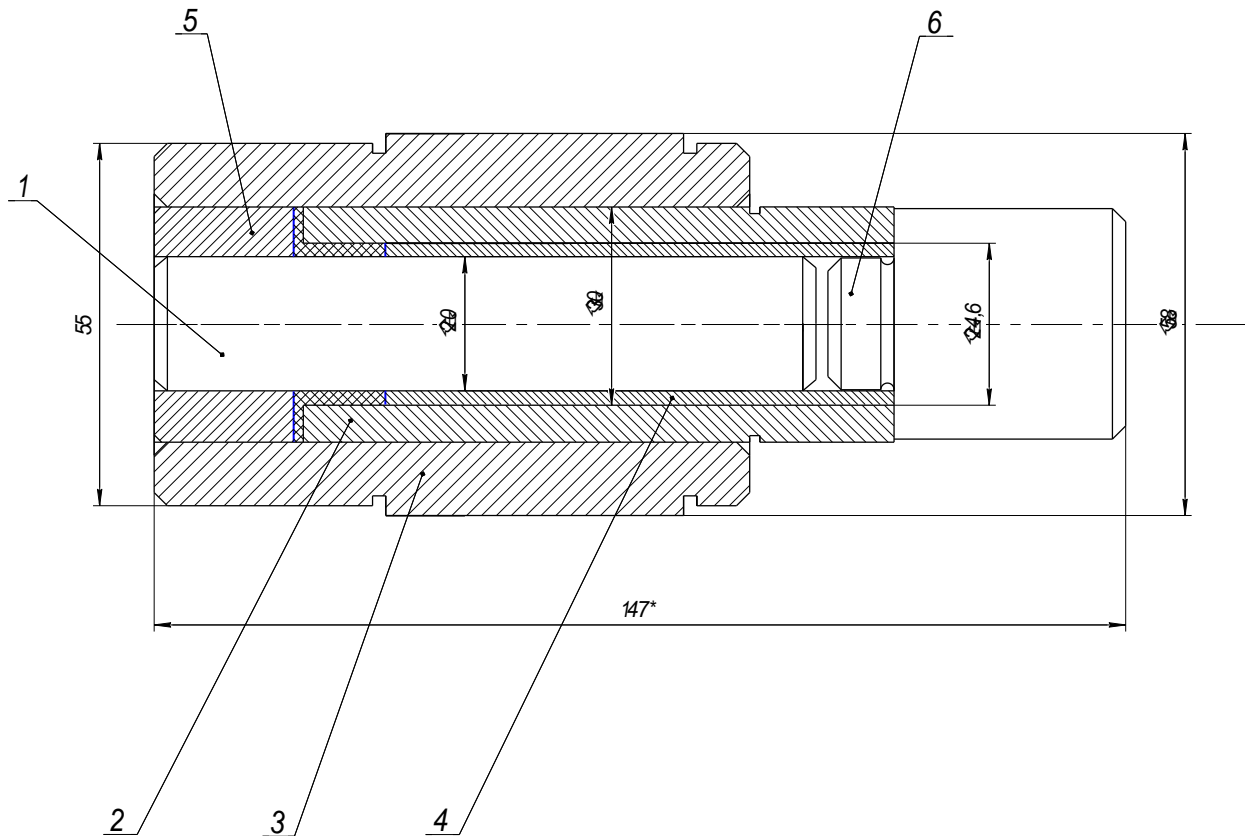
Пристосування для пресування втулок маятникового важеля:
